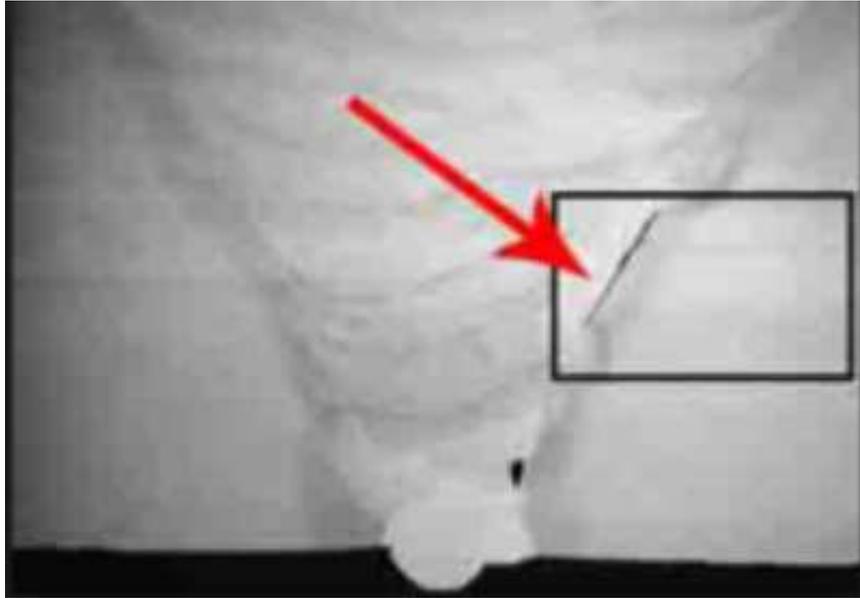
18. Falta de fusión vista en la radiografía de una soldadura.
